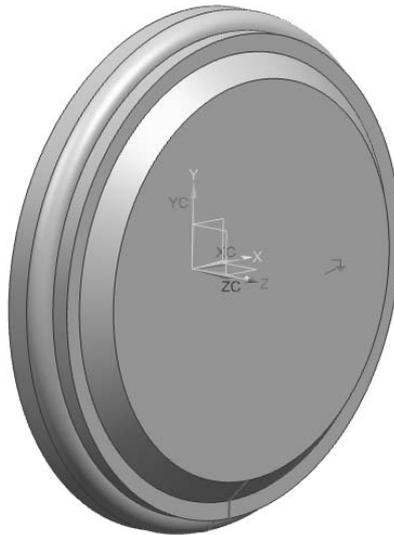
Исходная инструментальная поверхность фасонной фрезы
